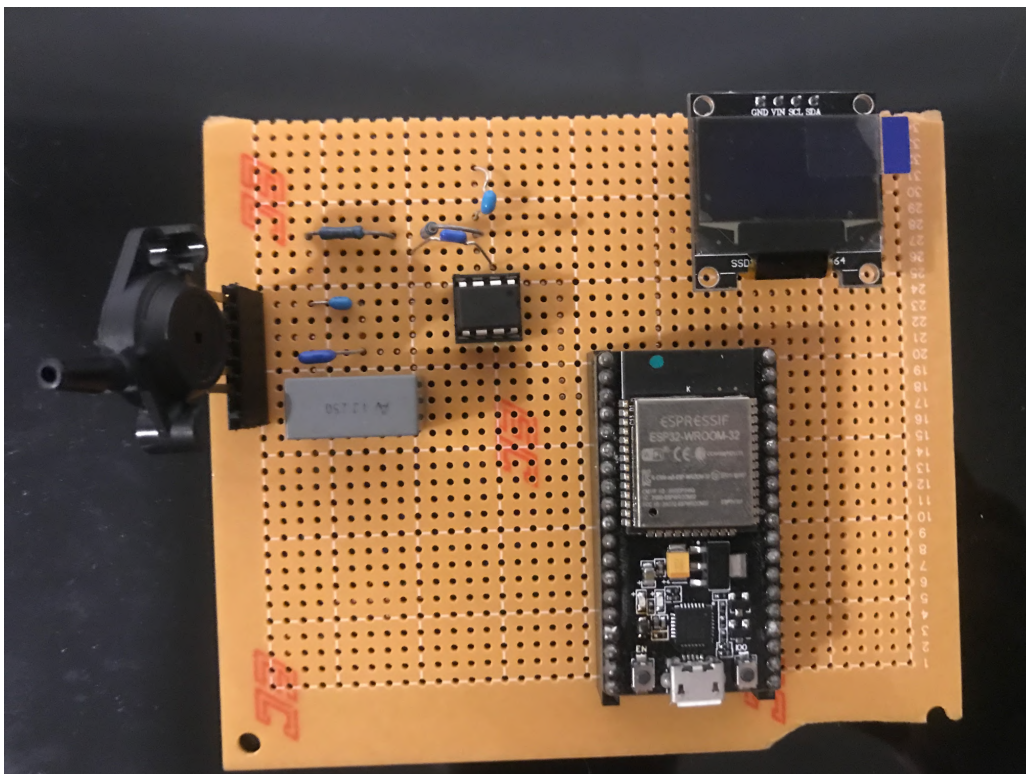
Placa de circuito impresso com o produto final (lado frontal)
